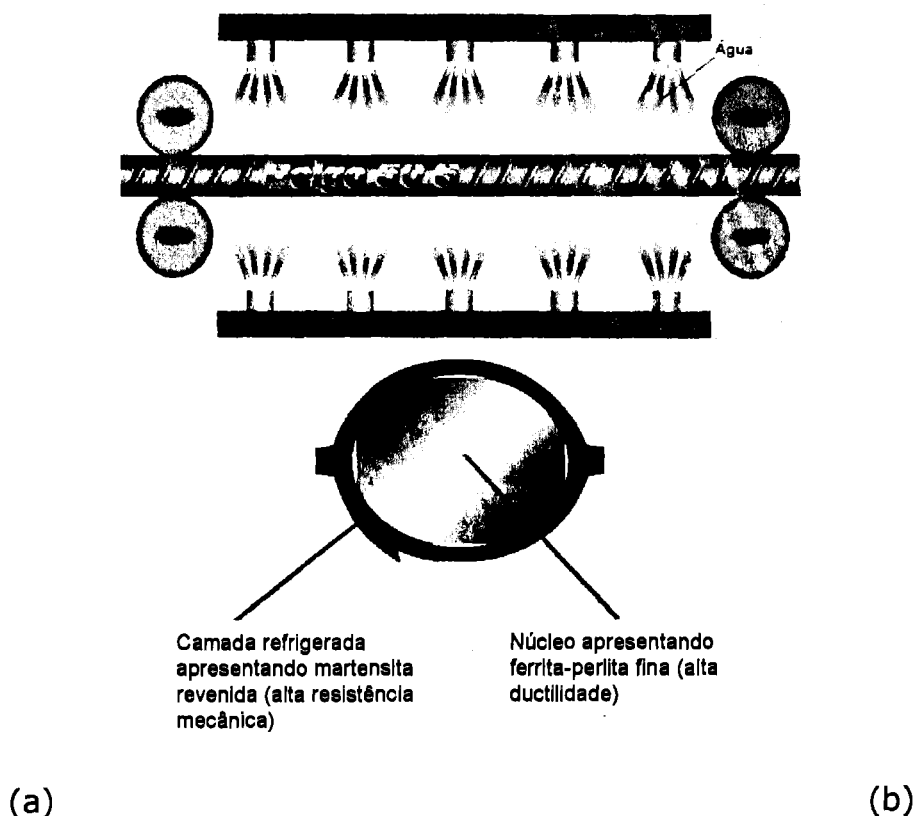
Ilustração do processo de fabricação do CA 50 soldável
